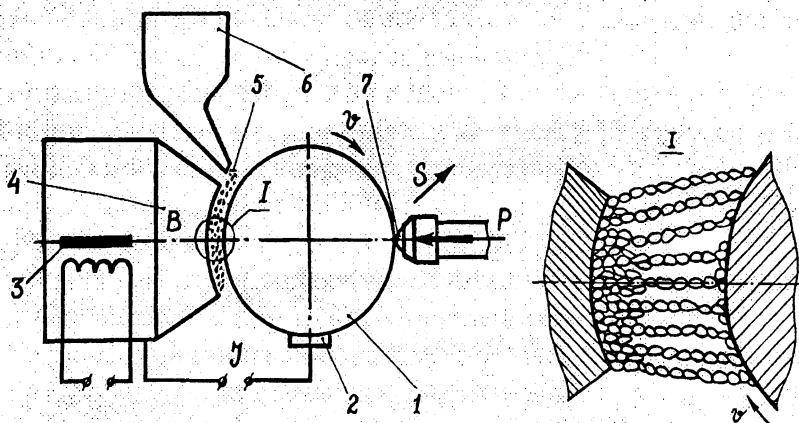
Электромагнитная наплавка с поверхностным пластическим деформированием: 1 – обрабатываемая деталь; 2 – скользящий контакт; 3 – электромагнит; 4 – полюсный наконечник; 5 – ферромагнитный порошок; 6 – дозирующее устройство; 7 – шариковый обкатник; V – скорость главного движения; S – скорость подачи; P – усилие деформирования; B – магнитная индукция; I – сила тока электродуговых разрядов
